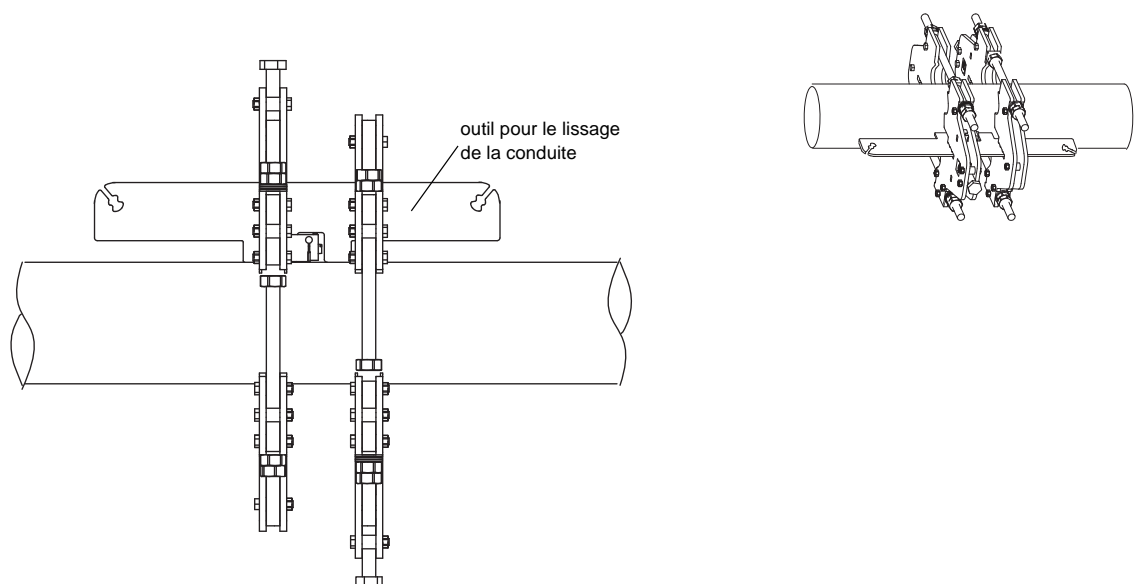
Positionnement des découpes pour lame de couplage des deux dispositifs de fixation à la conduite
